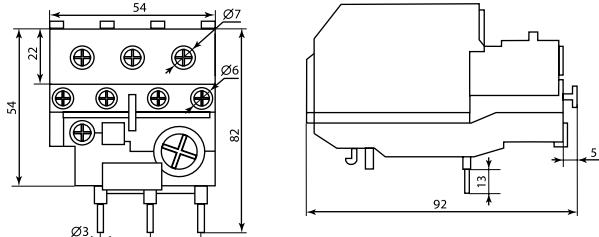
Габаритные и установочные размеры реле РТИ-3353 (для 32 А)
